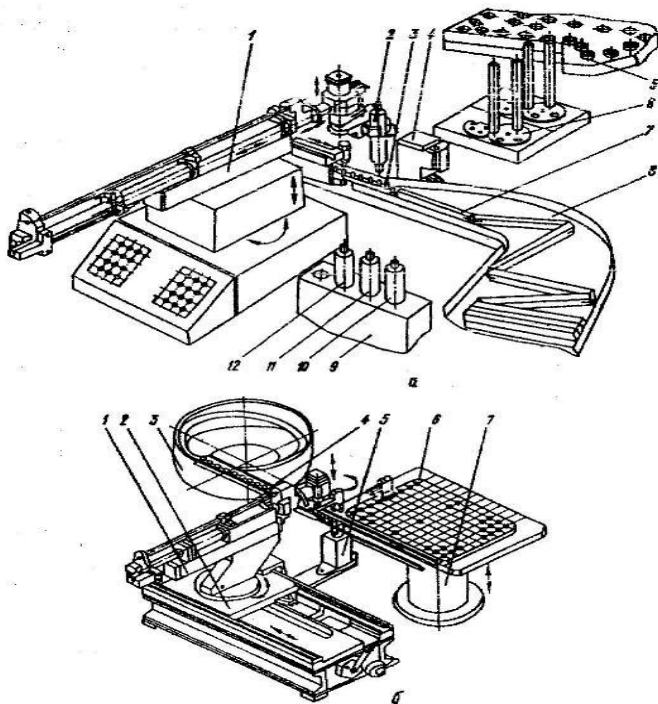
Компоновка РТК: а – для сборки клапанов; б – для укладки заготовок постоянных магнитов в кассеты
